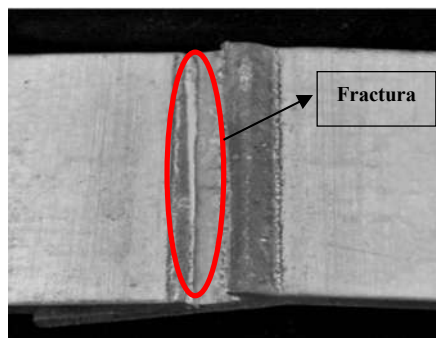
Fractura en la unión de soldadura del acero CP 780 [18].
